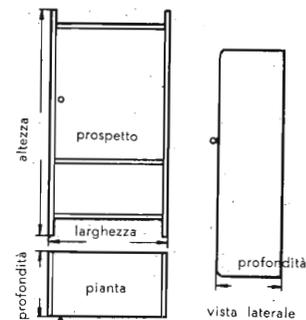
Disegno esecutivo: prospetto, pianta, vista laterale.
